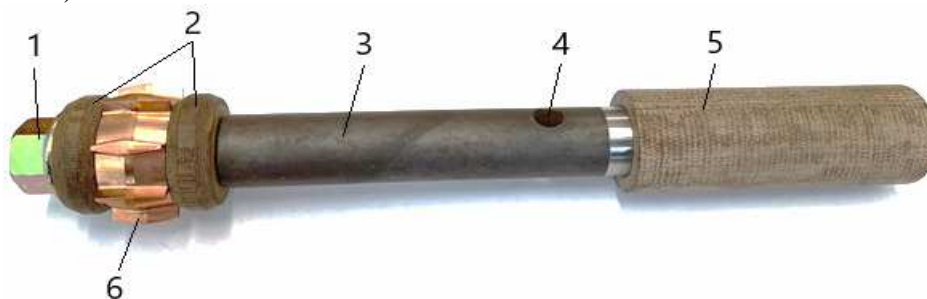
Инструмент для электрохимической закали рабочих поверхностей шлицевой муфты (патент RU2572677C1): 1 – гайка, 2 – направляющие токоизолирующие втулки, 3 – оправка, 4 – отверстие для крепления токопроводящей шины, 5 – токоизолирующая втулка, 6 – упрочняющие элементы
